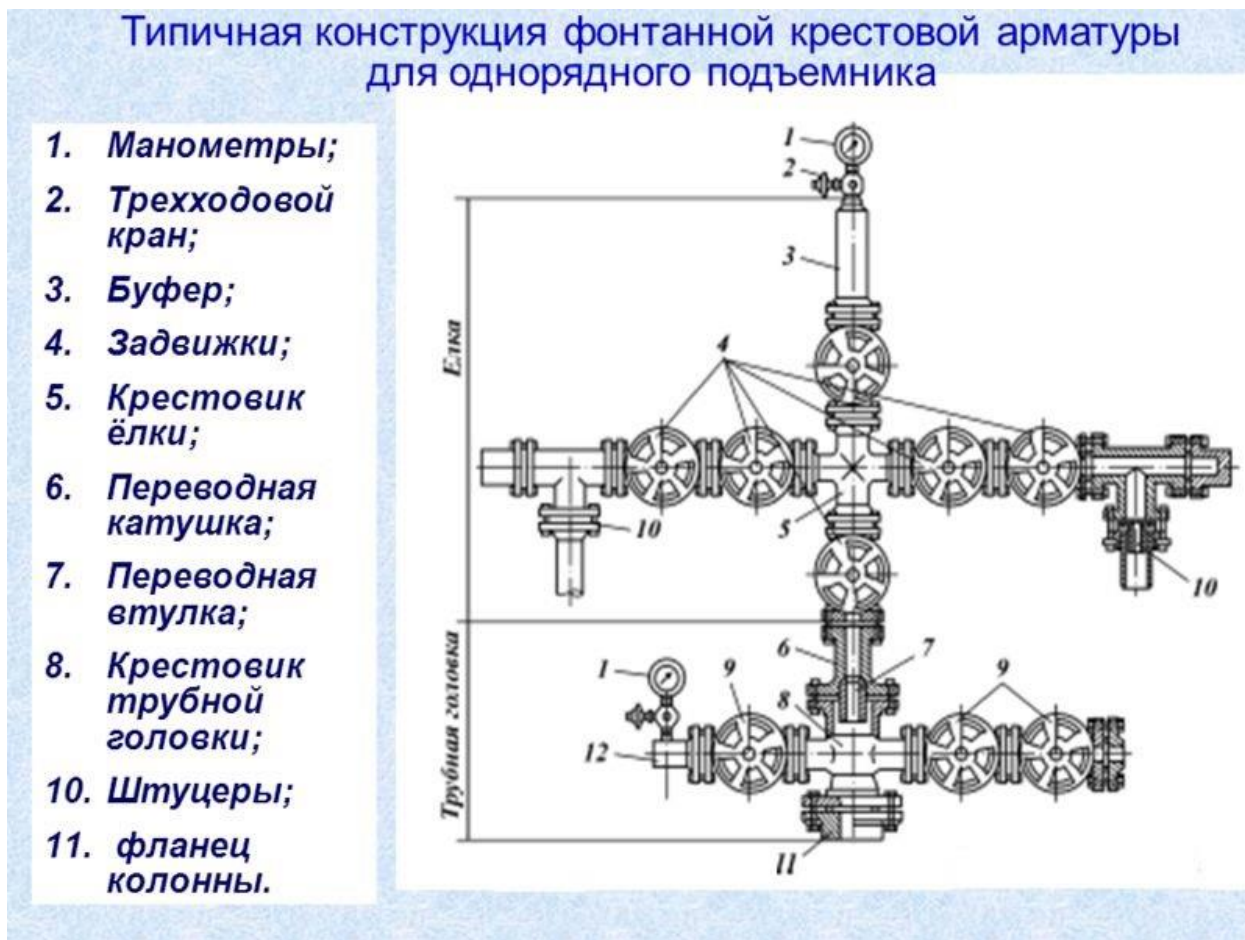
Конструкция фонтанной крестовой арматуры для однорядного подъемника
